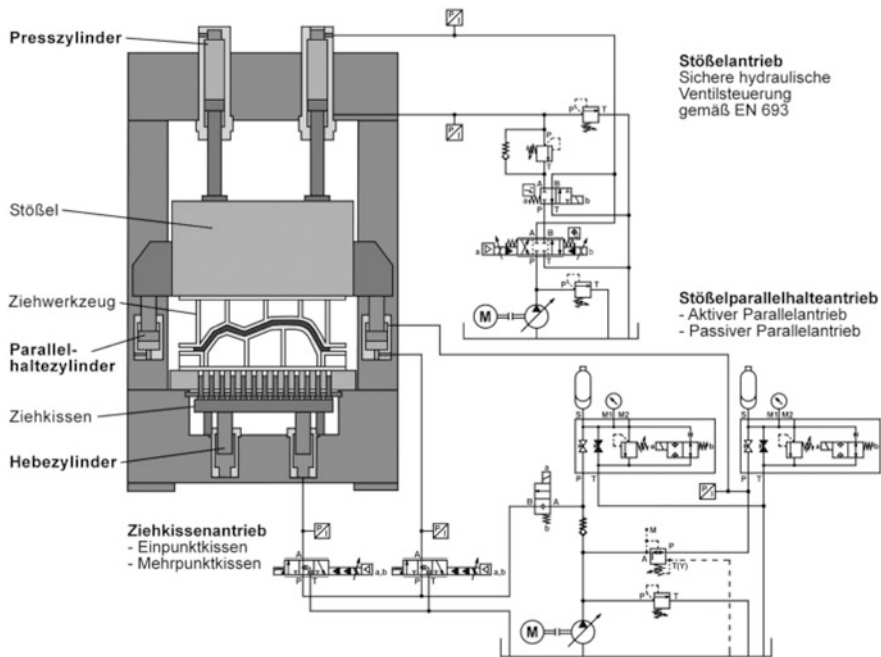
Hydraulische Tiefziehpresse mit eingebautem Tiefziehwerkzeug und Übersichtsschaltplan einer hydraulischen Pressensteuerung nach Bosch Rexroth [64] und Schuler [62]
